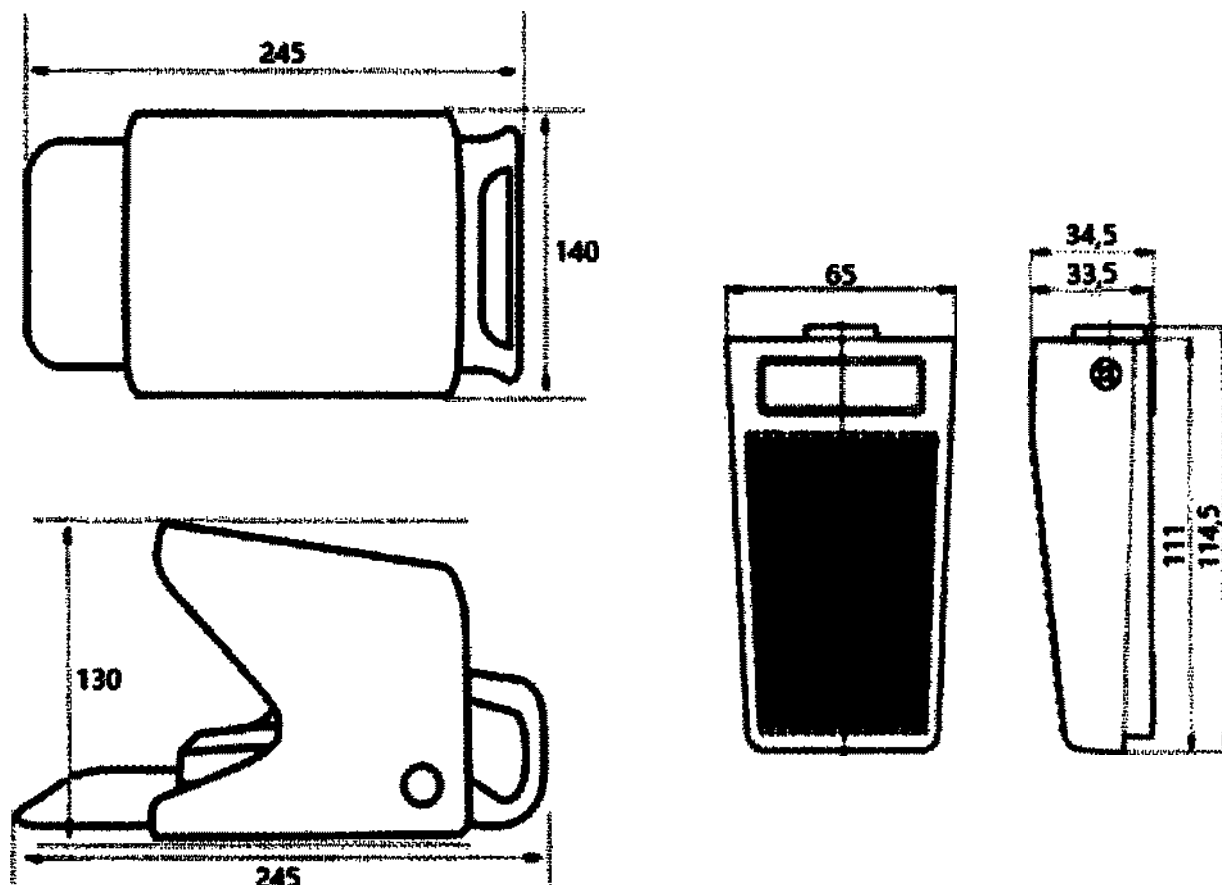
Схематических чертеж педали ножной HI-REX с габаритными размерами
